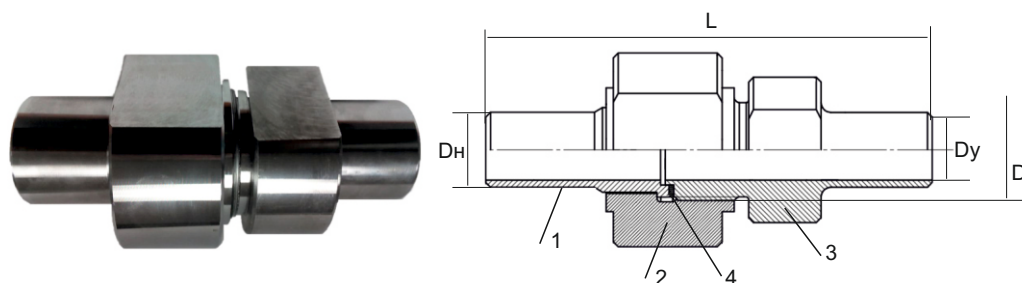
Ниппель для установки насадка на выпускном трубопроводе
